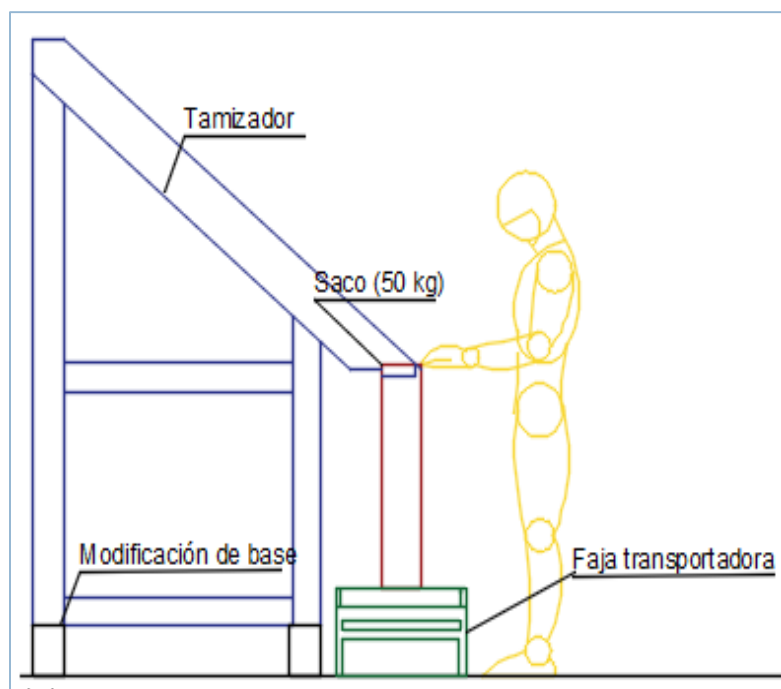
Puesto de trabajo de llenado y pesado – Vista lateral propuesto
